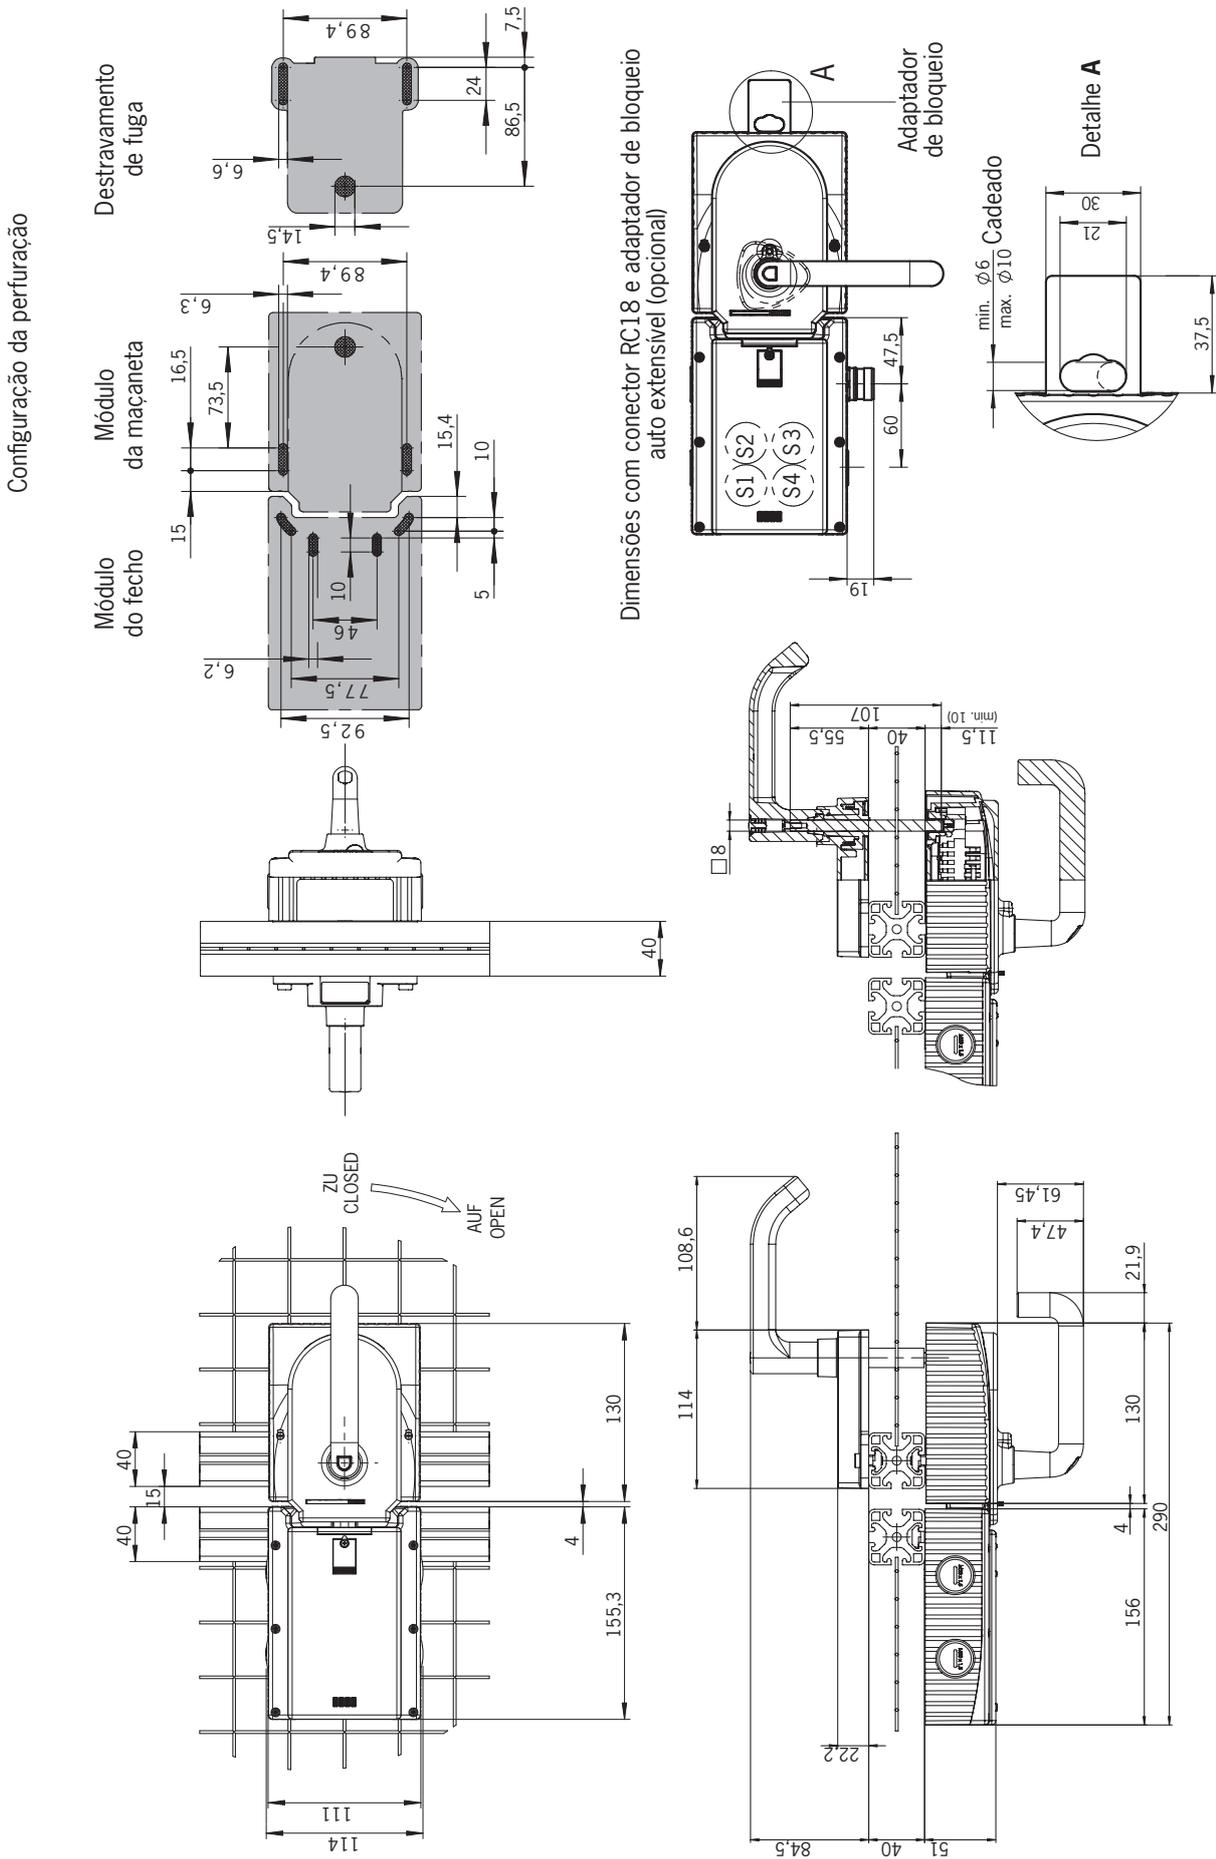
Desenho dimensional MGB montado, sem placas de montagem opcionais
